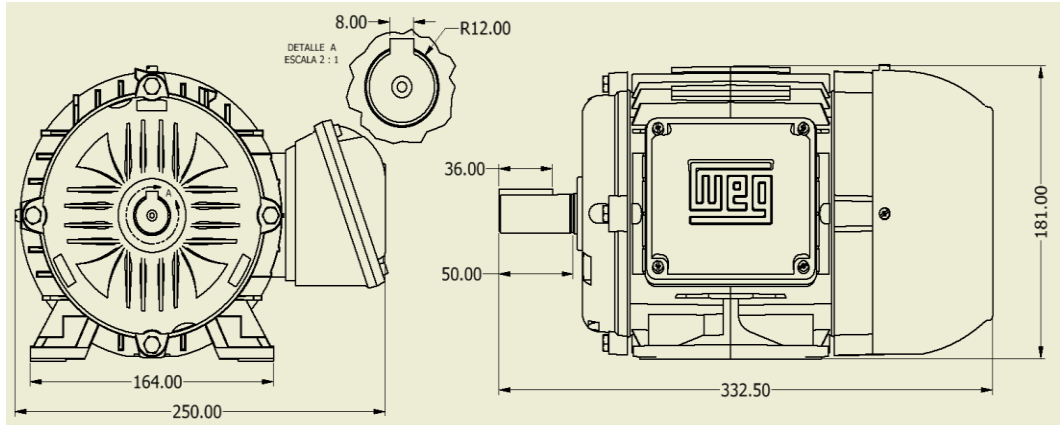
Principales dimensiones de motor (Weg®, 2021)
